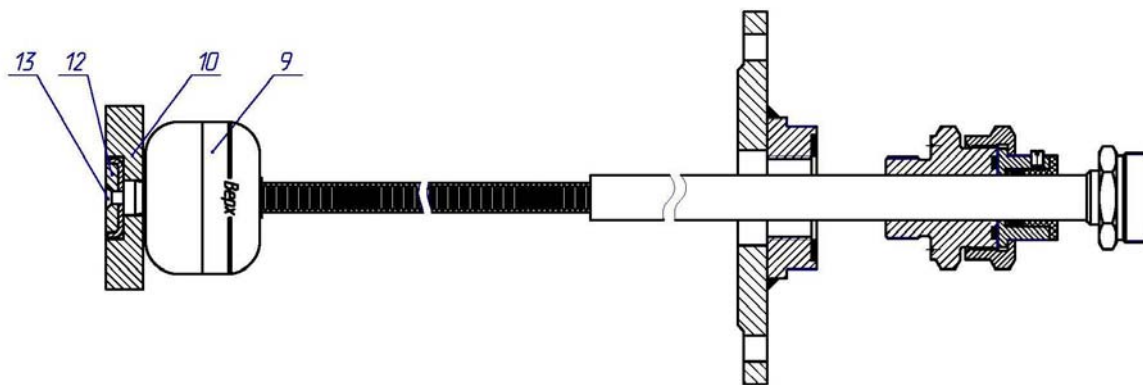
Установка поплавков, груза и магнита на внешнем корпусе уровнемера
